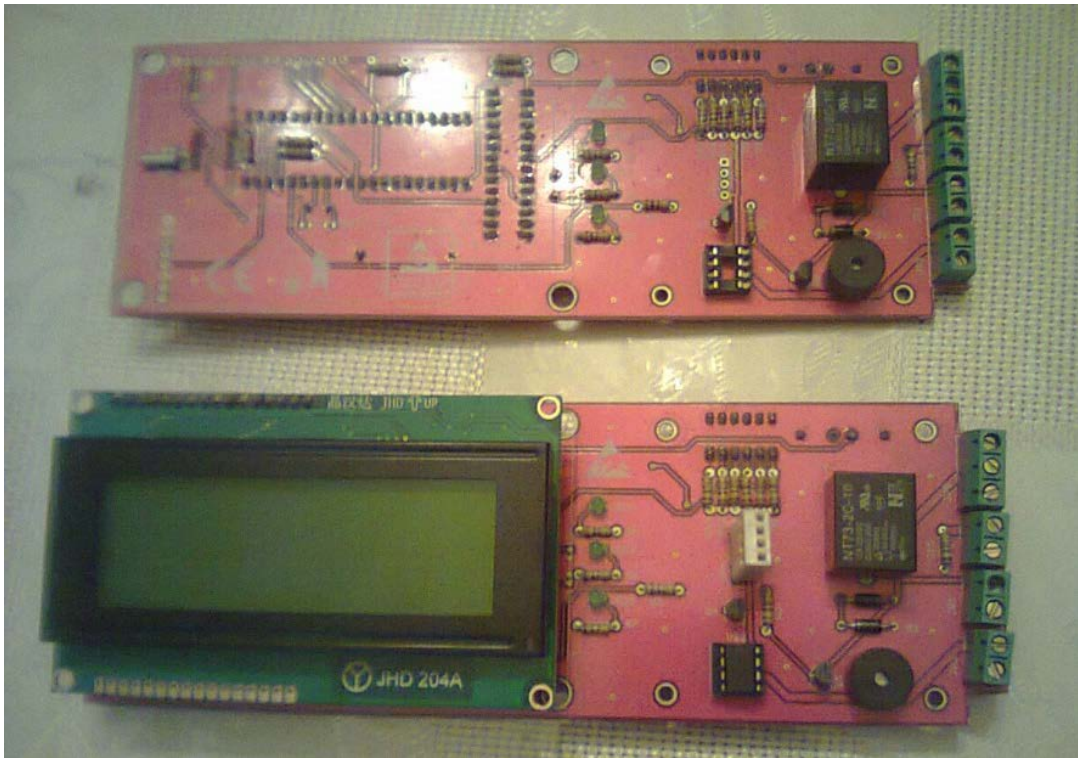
Diseño PCB Modulo Registro de Datos (3)
